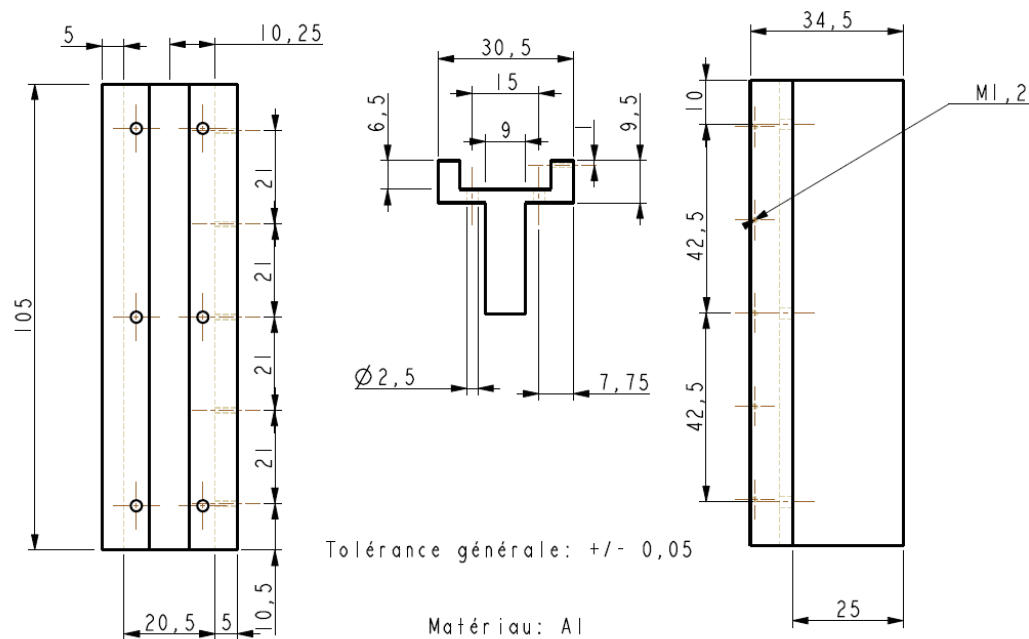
Dessin technique du support de l'échantillon (dimensions en mm)
